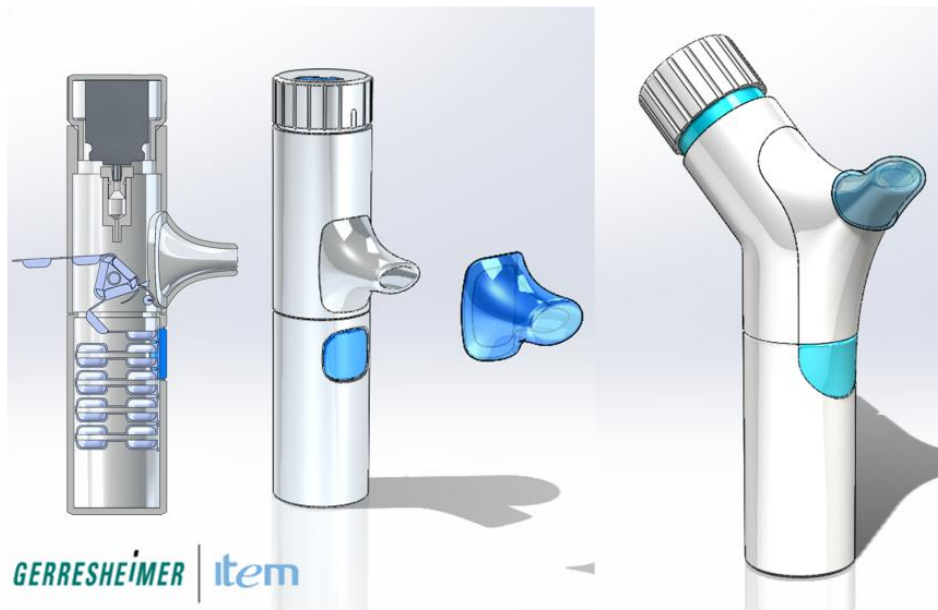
Entwurf 1 in einer zylindrischen oder leicht abgewinkelten Form
